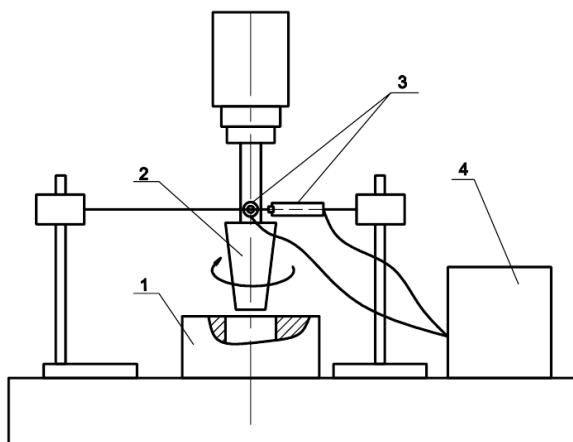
Схема вимірювань коливань інструменту щодо деталі під час її обробки:
